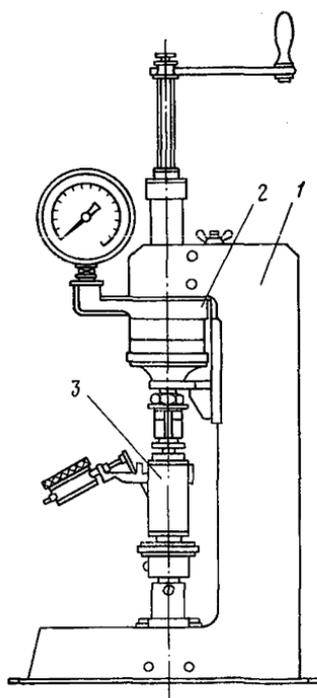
Тарировочное приспособление для прибора ГПНС-4
